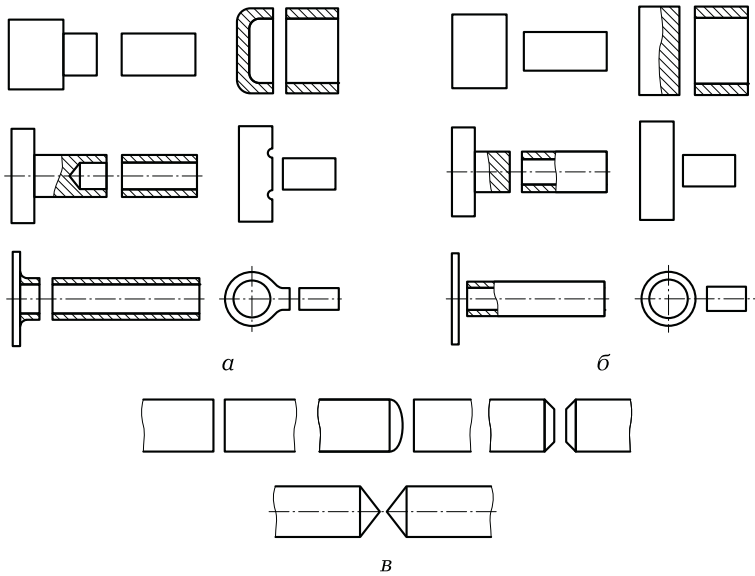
Конструктивное выполнение деталей для контактной стыковой сварки:
